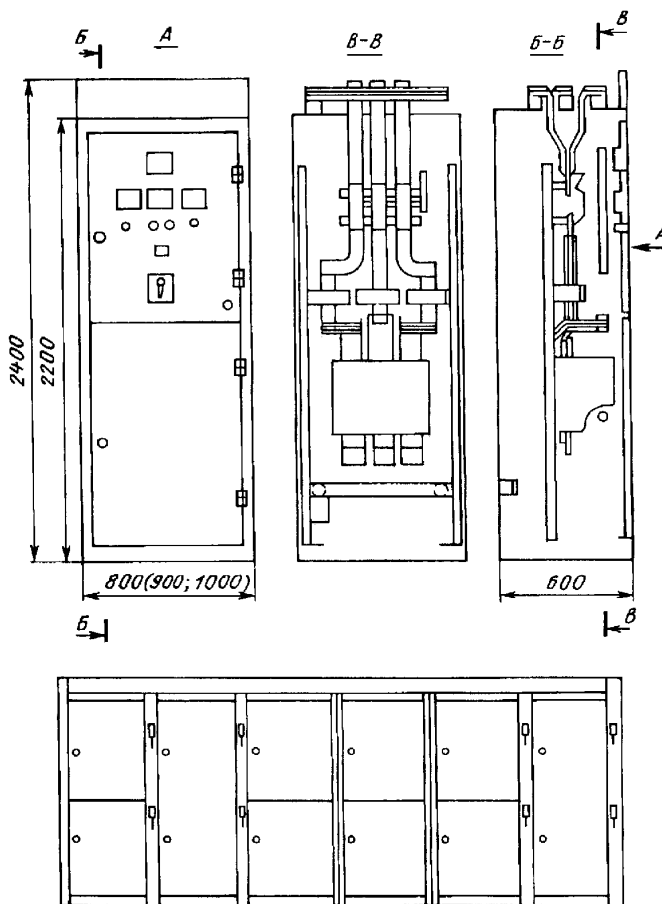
Габаритные размеры шкафа и общий вид щита V1
